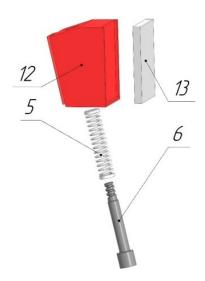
Клиновый контактный элемент ГЗУ: 5 – крепежный винт; 6 – возвратная пружина; 12 – опорное основание; 13 – накладка из упругоподатливого материала
